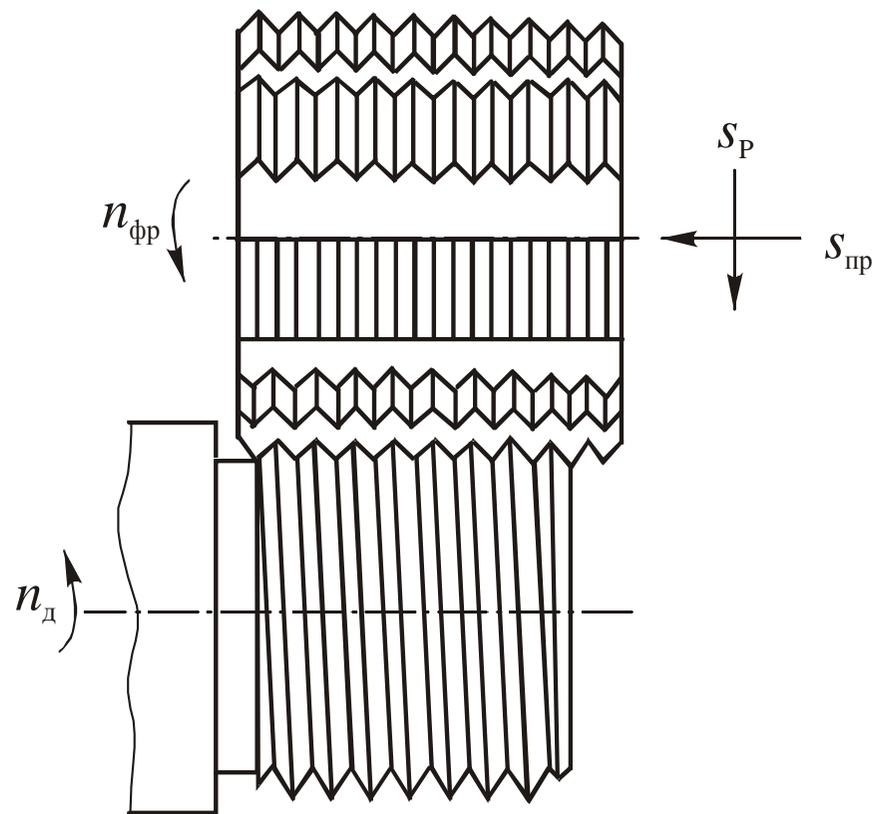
Схема нарезания резьбы гребенчатой фрезой
